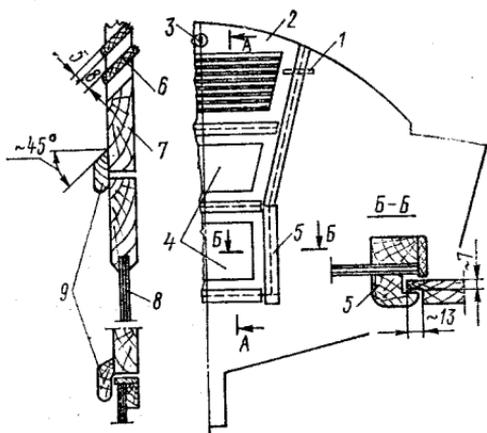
Конструкция задвижного щитка для входа в рубку.
